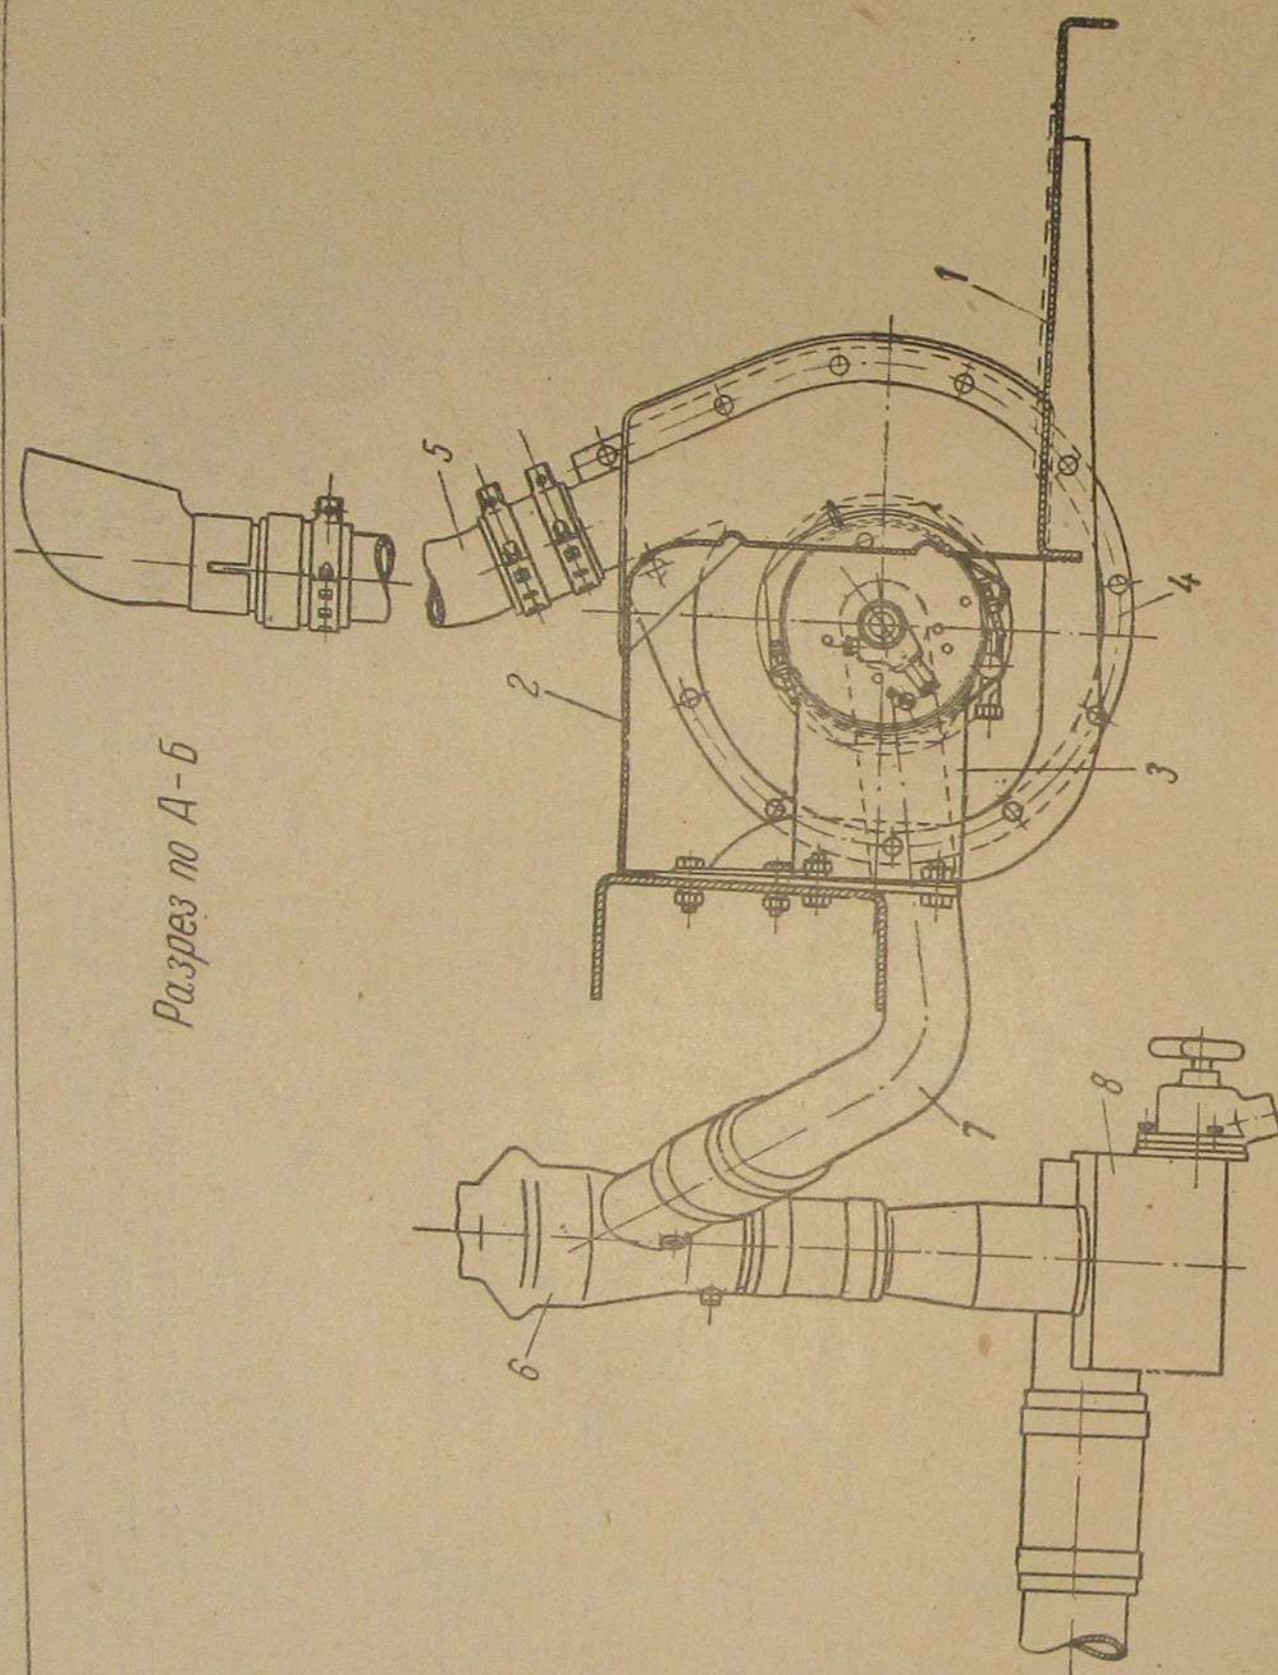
Установка вентилятора и смесителя ЗИС-13 на шасси ЗИС-21;
